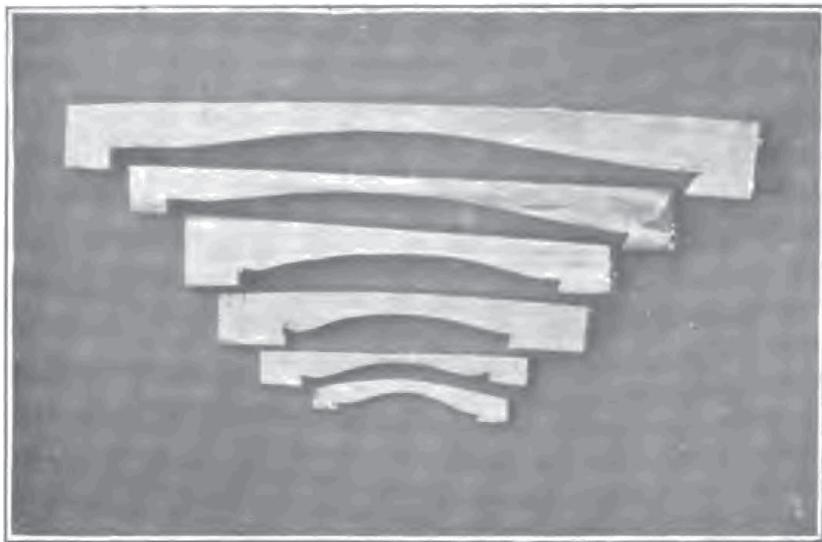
SÉRIE DE SERRE-JOINTS OU ENTAILLES.
